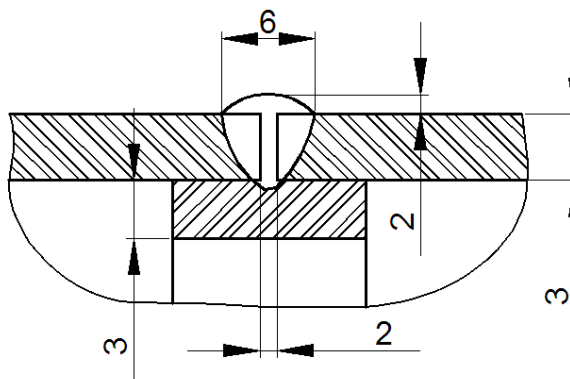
Схема зварного стикового з'єднання С5 за ГОСТ 8713-79
